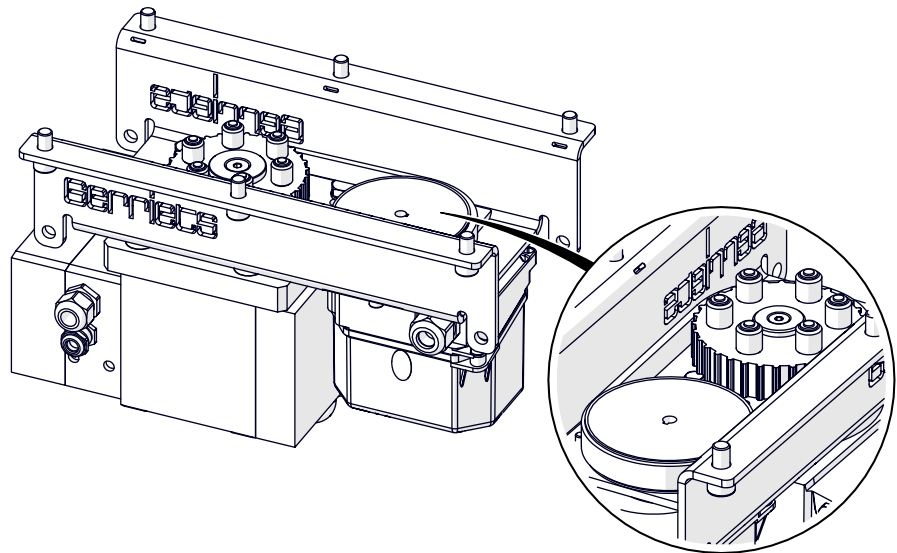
Kompakt-Getriebemotor – BELT DRIVE BT-30
